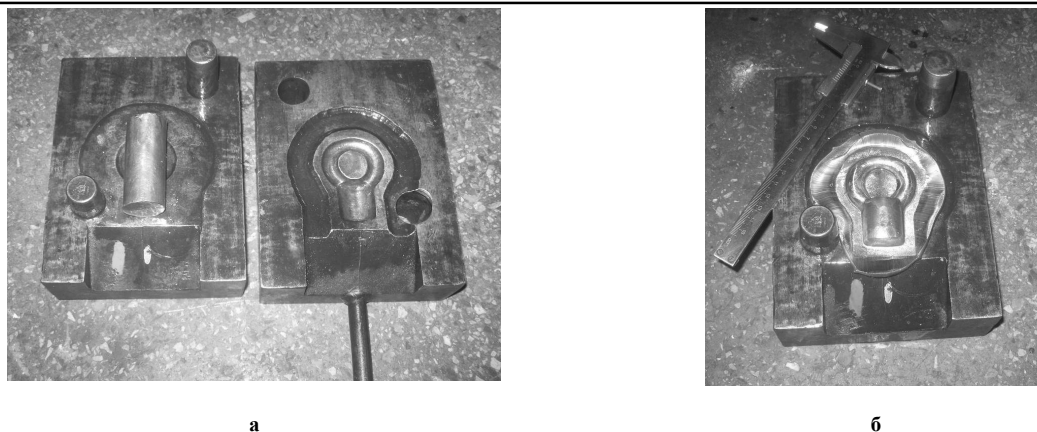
Штамповка поковки «рым - болт» по базовой технологии:
